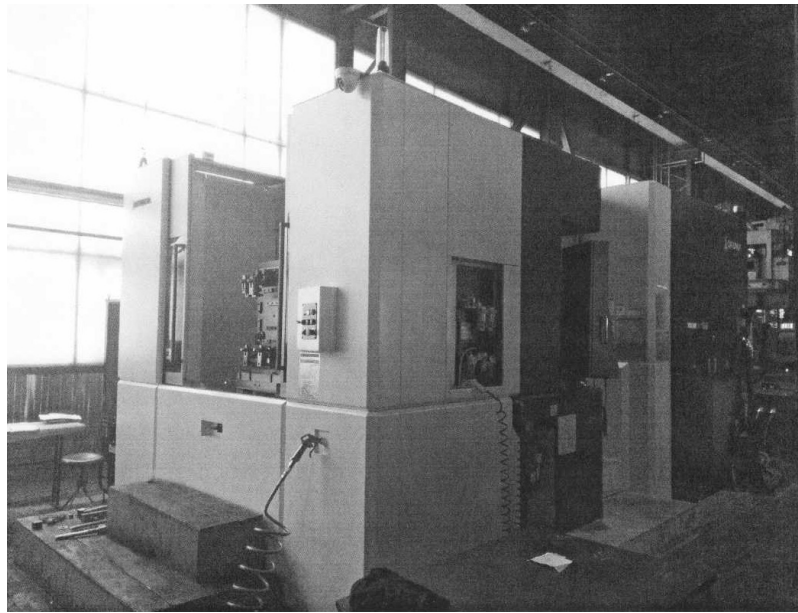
Горизонтально – фрезерувальний обробний центр OKUMA MA-600H
